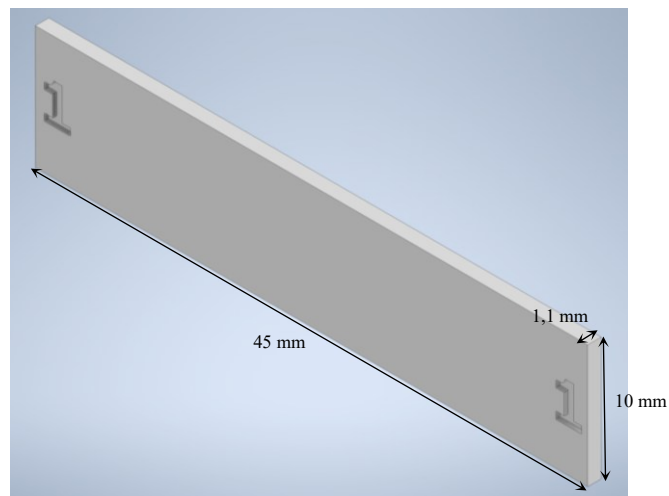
Modello CAD e dimensioni dei campioni di cute sintetica per il test di trazione del punto di sutura.
